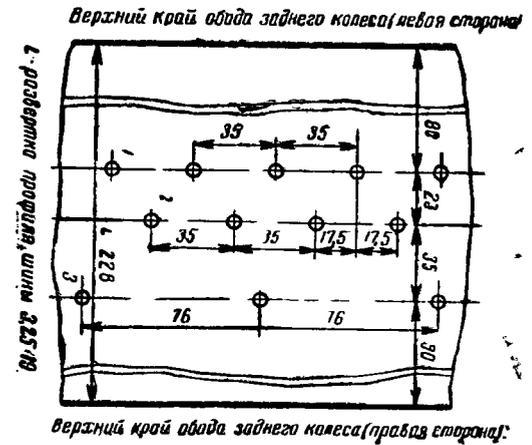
Расположение шипов на шине заднего колеса; 1—первый ряд с левой стороны колеса; 2—второй ряд; 3—третий ряд шипов.
